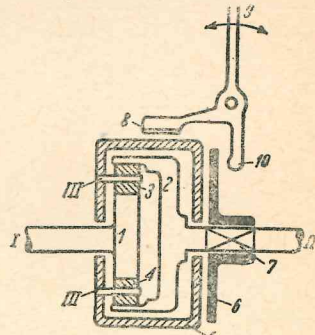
в. Схема реверсивной муфты с планетарными колесами
